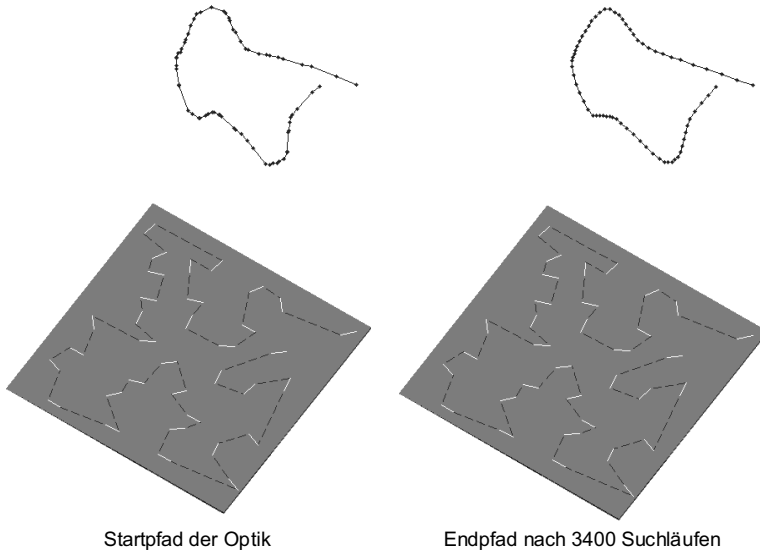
Wirkungsweise des Teilverfahrens zur Glättung des Optikpfades anhand eines Beispiels mit 34 Schweißnähten
